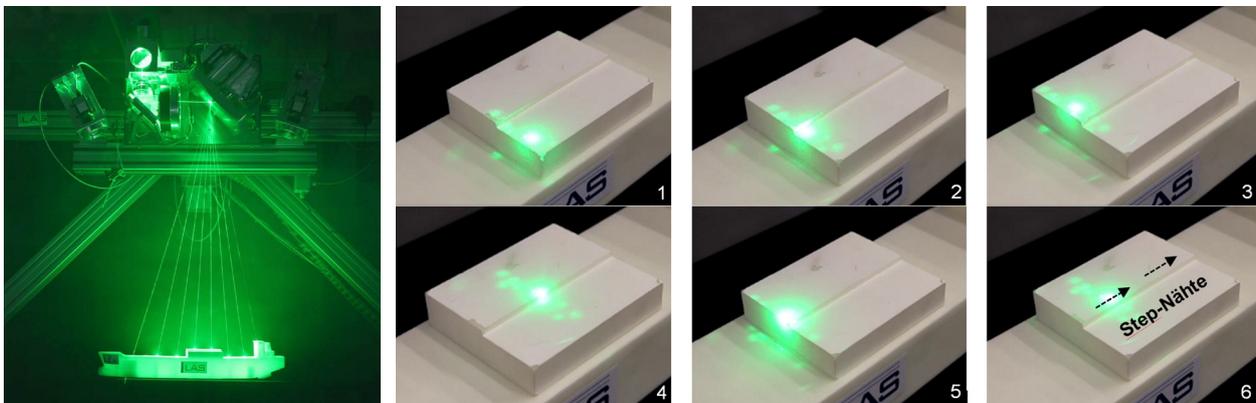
Funktionsfähiger Laser-Remote-Fertigungsdemonstrator mit aktivem grünen Messlaser beim Analyseprozess eines „Bauteils“ (links), Vermessung der Konturen zum Laser-Remote-Step-Nahtschweißen am Überlappstoß (rechts) (Quelle: iLAS)
